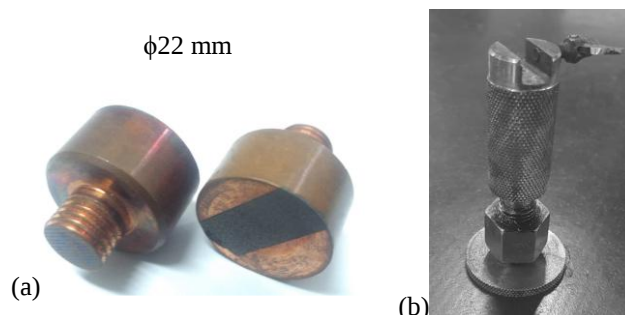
Ferramental empregado a) eletrodo-ferramenta e b) Sistema de fixação dos corpos de prova.
